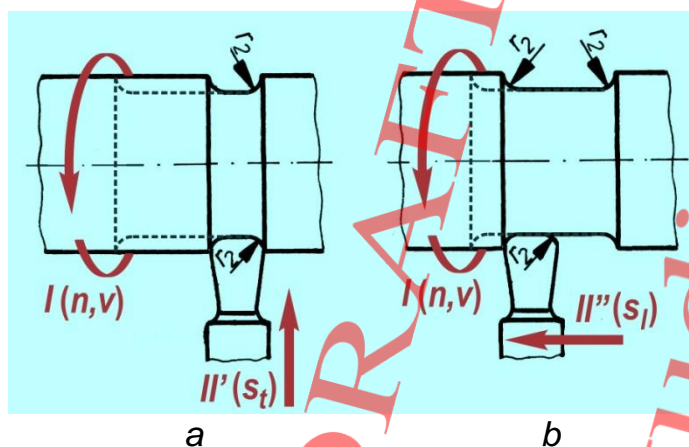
Strunjirea canalelor late: (a) etapa avansului de pătrundere; (b) etapa strunjirii longitudinale
